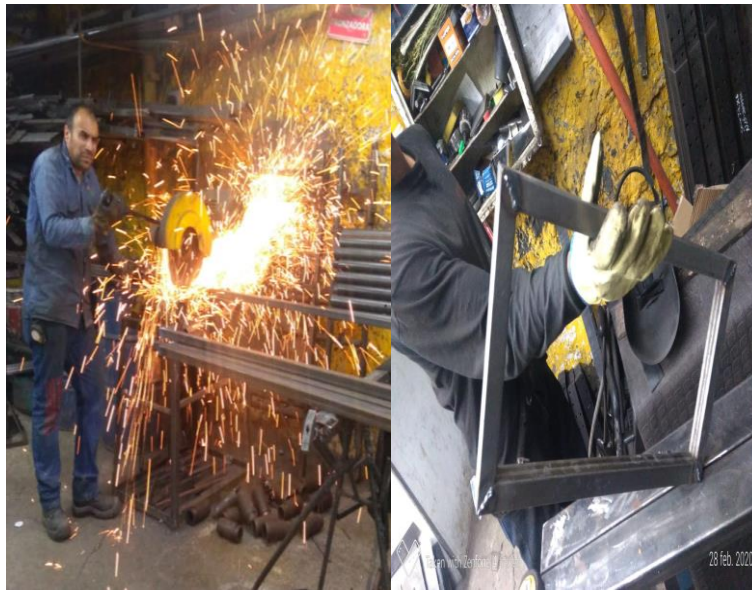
Soldadura marco para mallas, fuente propia
